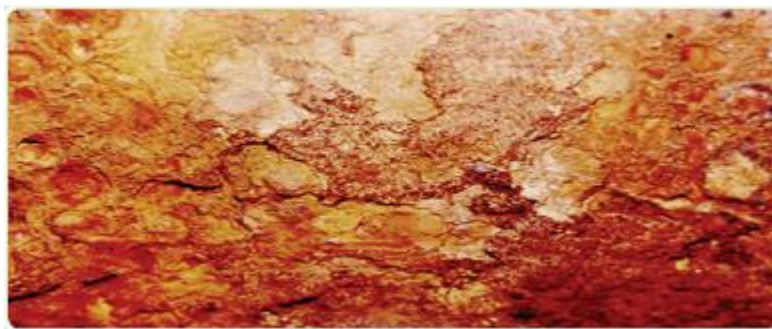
Corrosão uniforme em chapa de aço-carbono.
